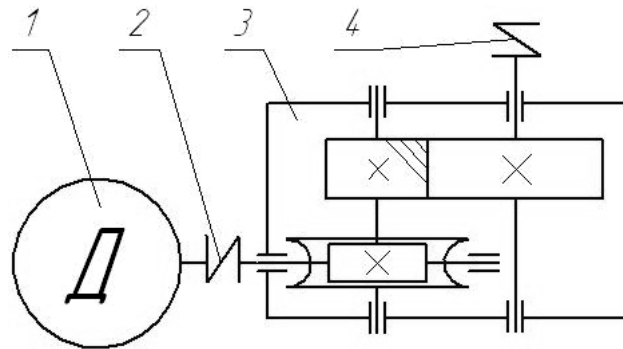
Кінематична схема черв'ячно-циліндричного привода
